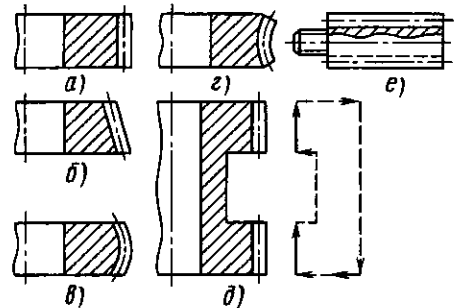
Зубчатые колеса и шлицевые валы, нарезаемые на зубофрезерном станке: цилиндрическое колесо: а – зуб стандартный; б – зуб конусный; в – зуб бочкообразный; г – червячное колесо; д – двухвенцовое цилиндрическое колесо; е – шлицевый вал
